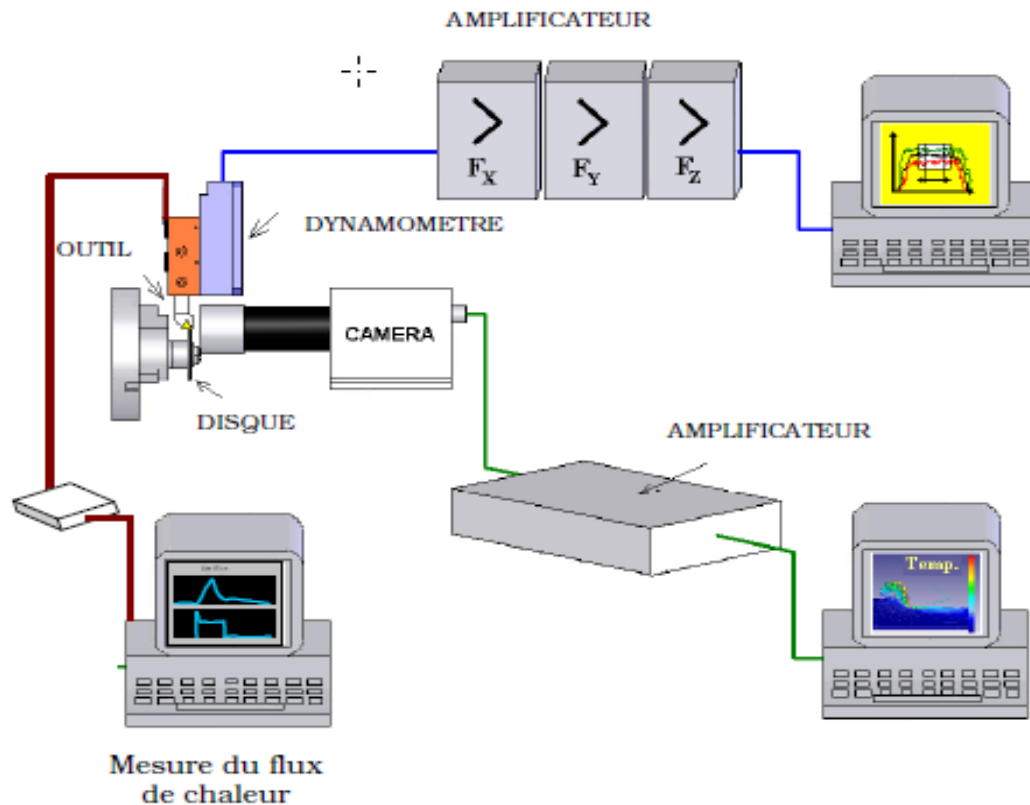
Instrumentation d'un dispositif de coupe orthogonale.
